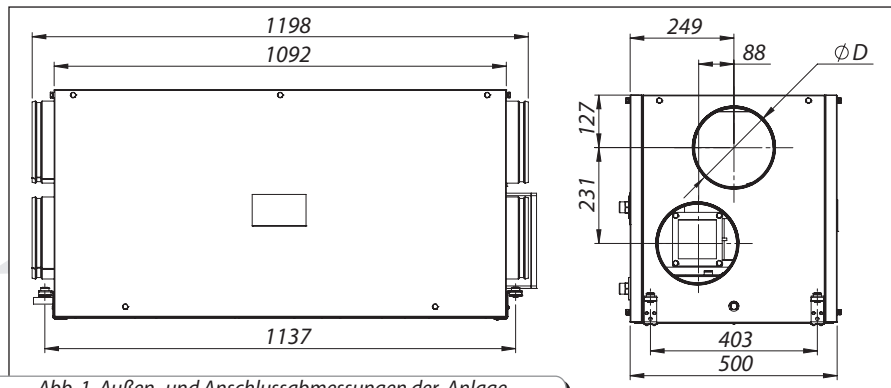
Außen- und Anschlussabmessungen der Anlage
